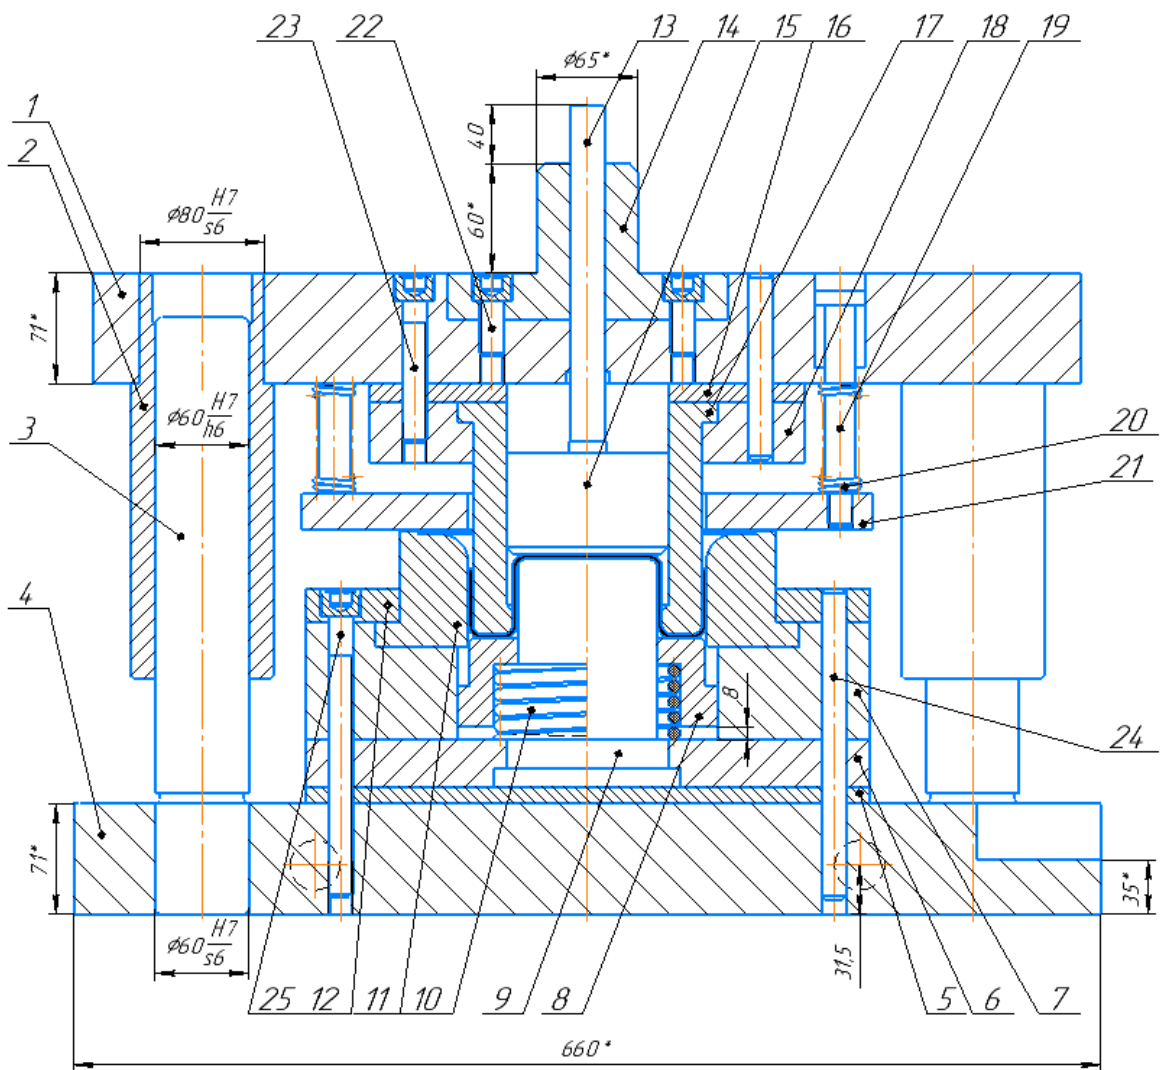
Общий вид штампа для обратной вытяжки:
